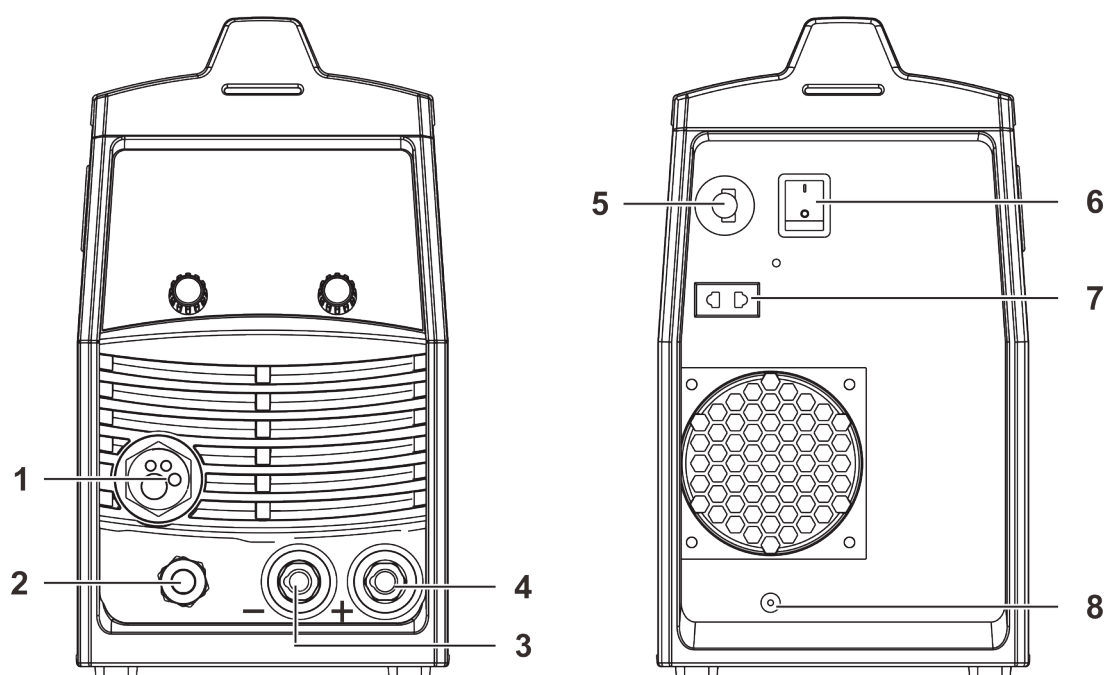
Общий вид (Инверторный сварочный полуавтомат)
